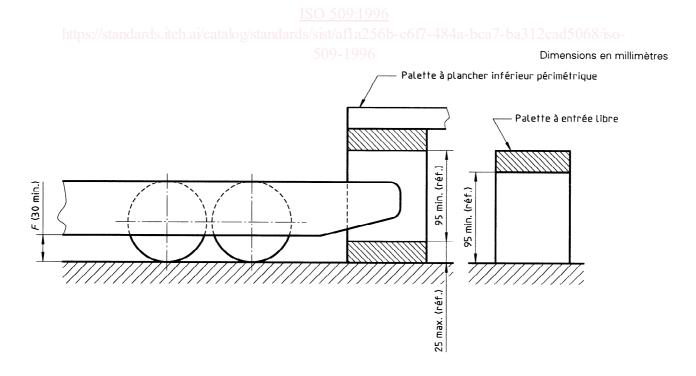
Détail de la garde au sol et des dimensions des palettes
